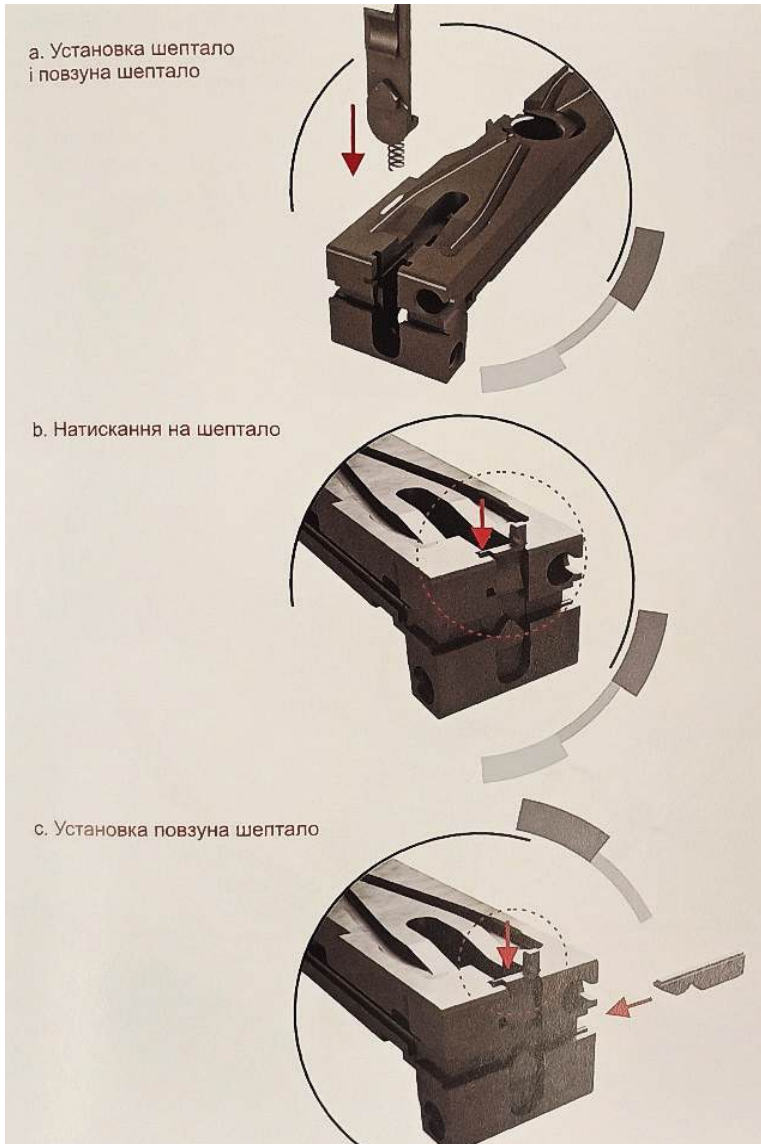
Установка шептало, повзуна шептало і пружини шептало в затворну раму в зборі
